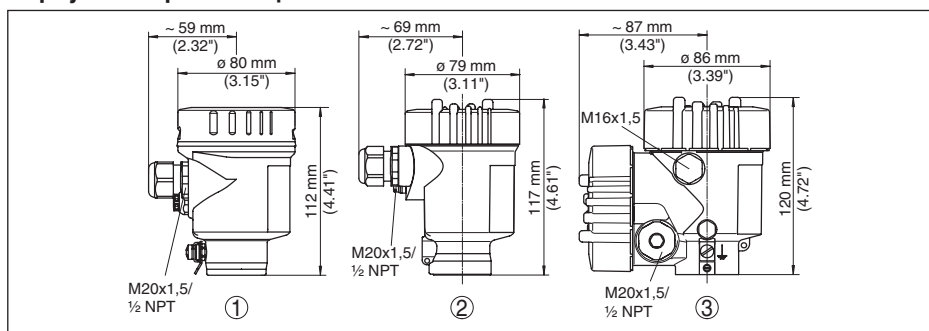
Корпуса в исполнении IP 66/IP 68 (0,2 bar) - с установленным модулем индикации и настройки корпус выше на 9 мм/0.35 in
